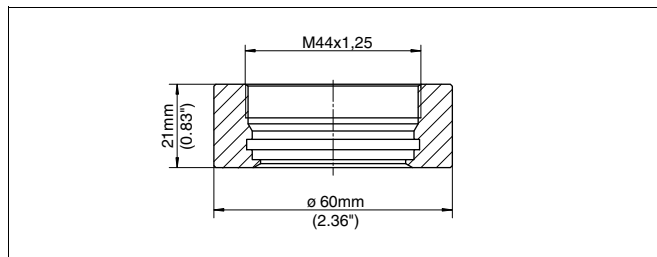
Medidas racor soldado M44 x 1,5
